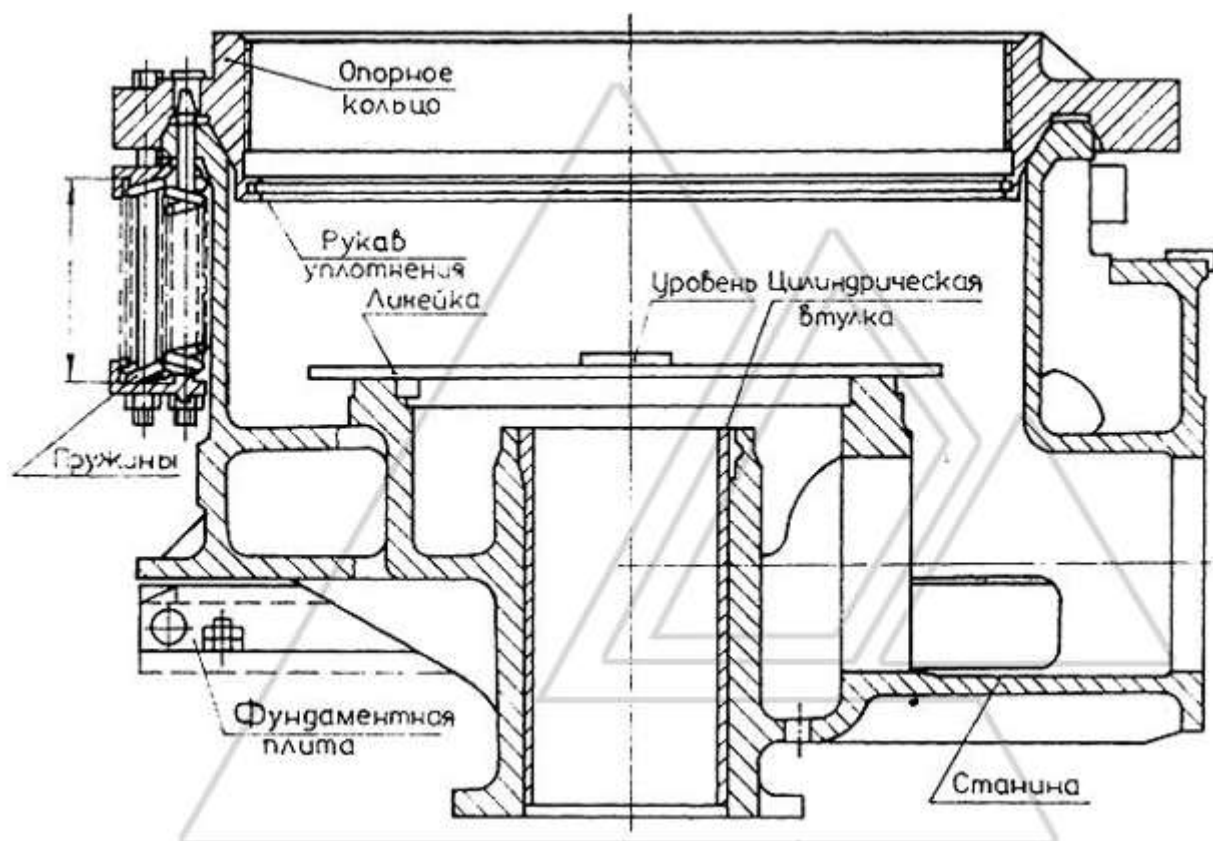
Монтаж станины в сборе с опорным кольцом и пружинами
